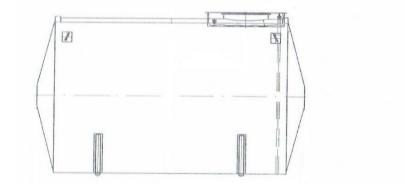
Общий вид резервуара РГС-10 зав.№ 114
